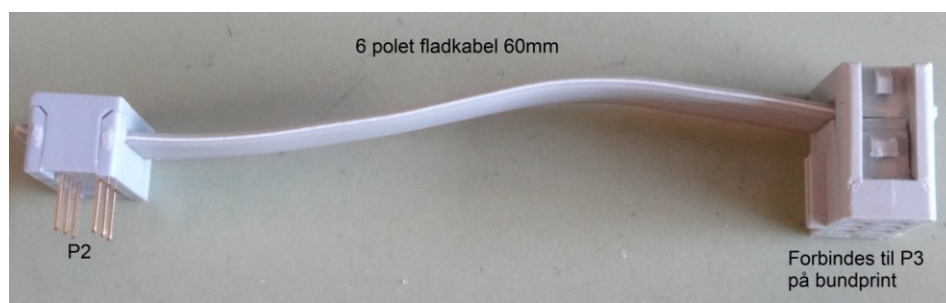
Forbindelseskabel forpladeprint – bundprint
